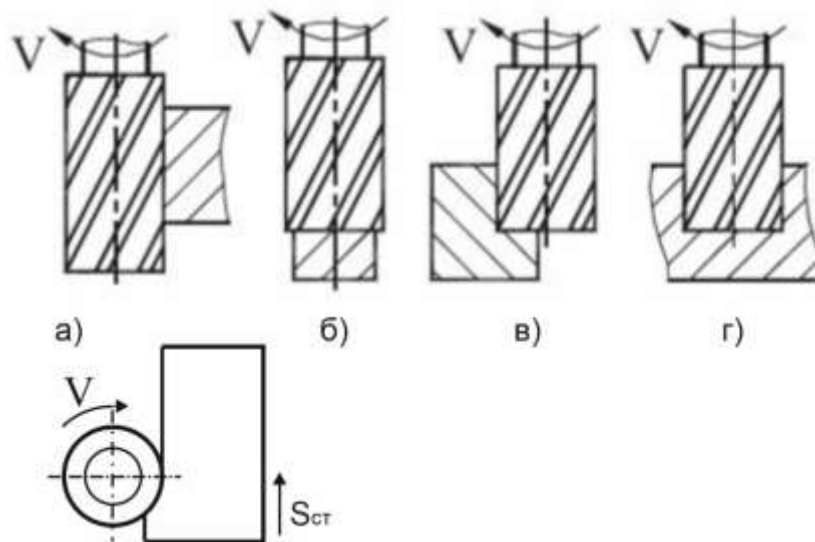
Схеми фрезерування кінцевими фрезами.
